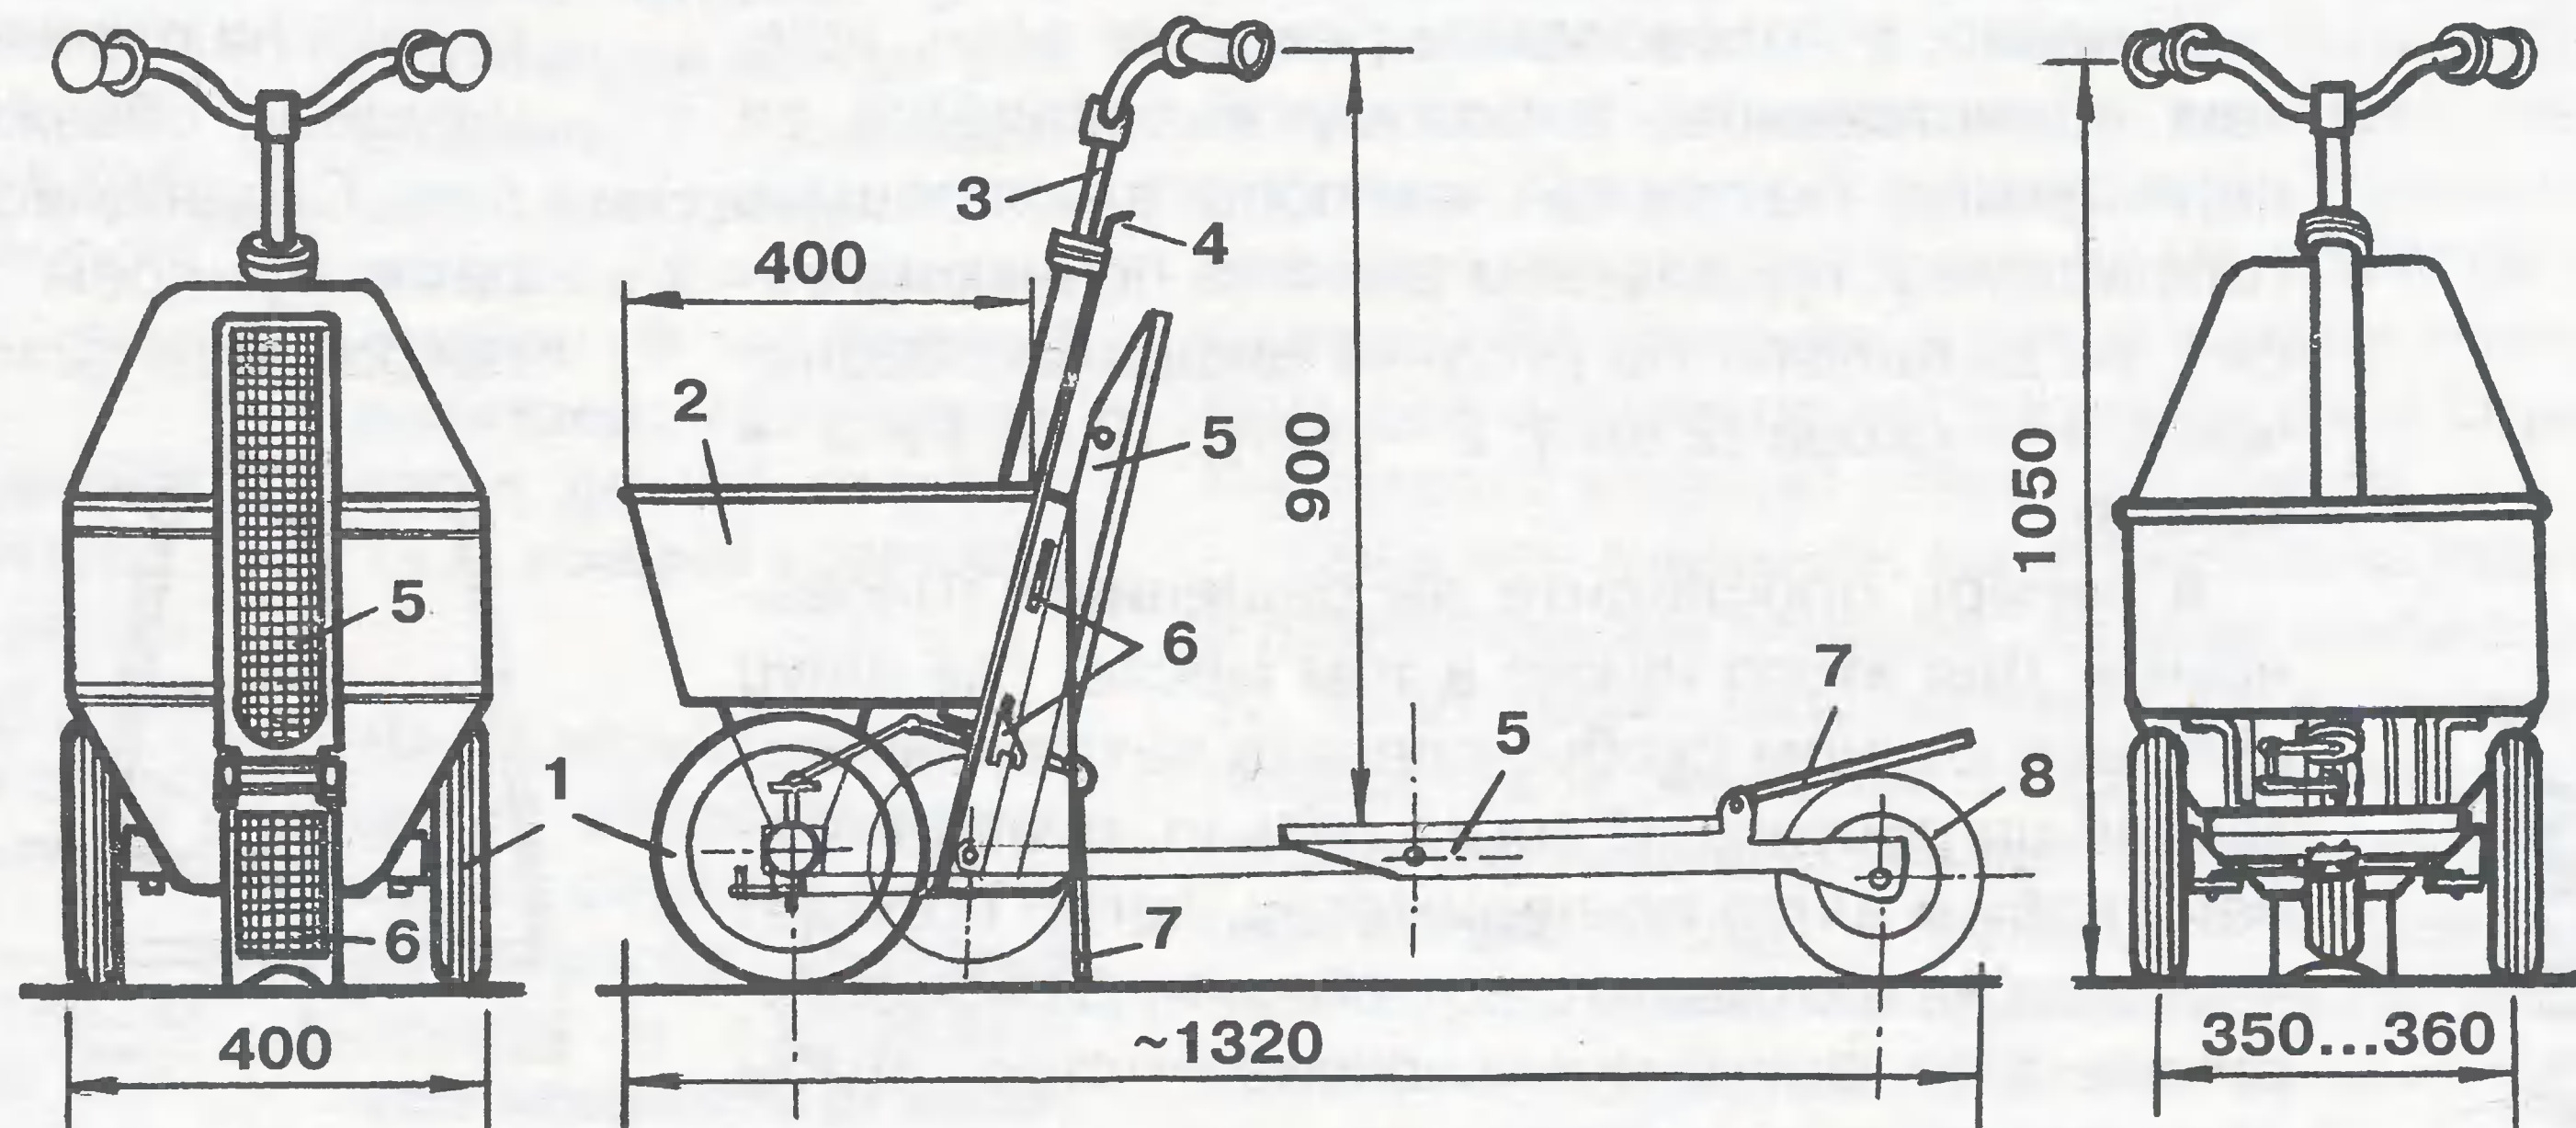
Основные размеры конструкции: 1 — рулевые колеса; 2 — кузов; 3 — руль; 4 — фиксатор руля; 5 — откидная платформа; 6 — фиксатор платформы; 7 — тормозная педаль-подставка; 8 — дополнительное колесо.
